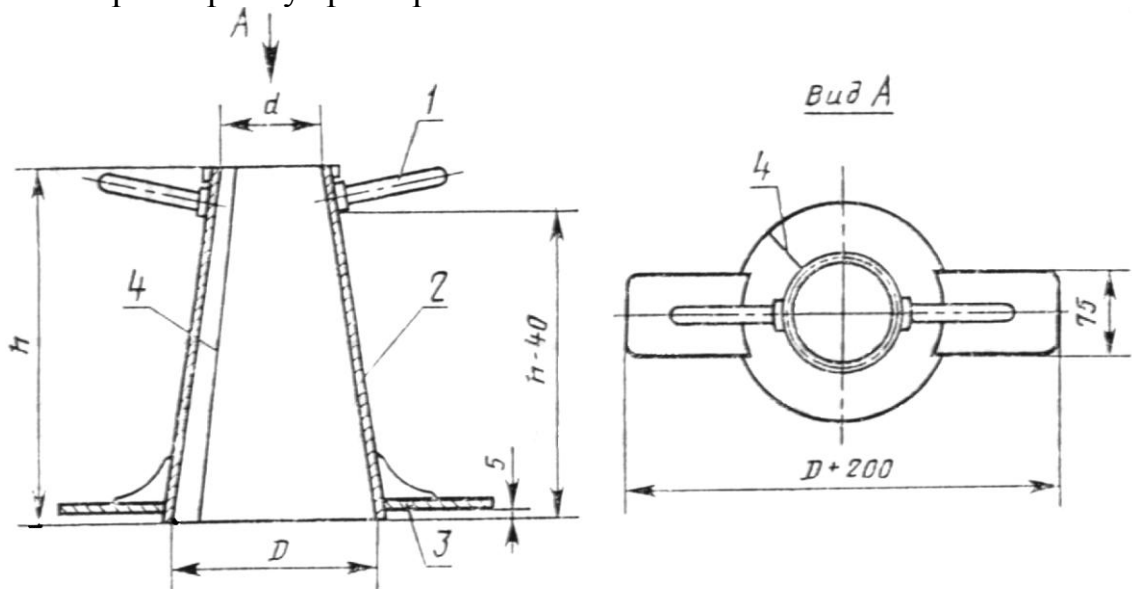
Стандартный конус для определения подвижности бетонной смеси: 1 - ручка; 2 - корпус прибора; 3 - упоры; 4 - сварной шов
